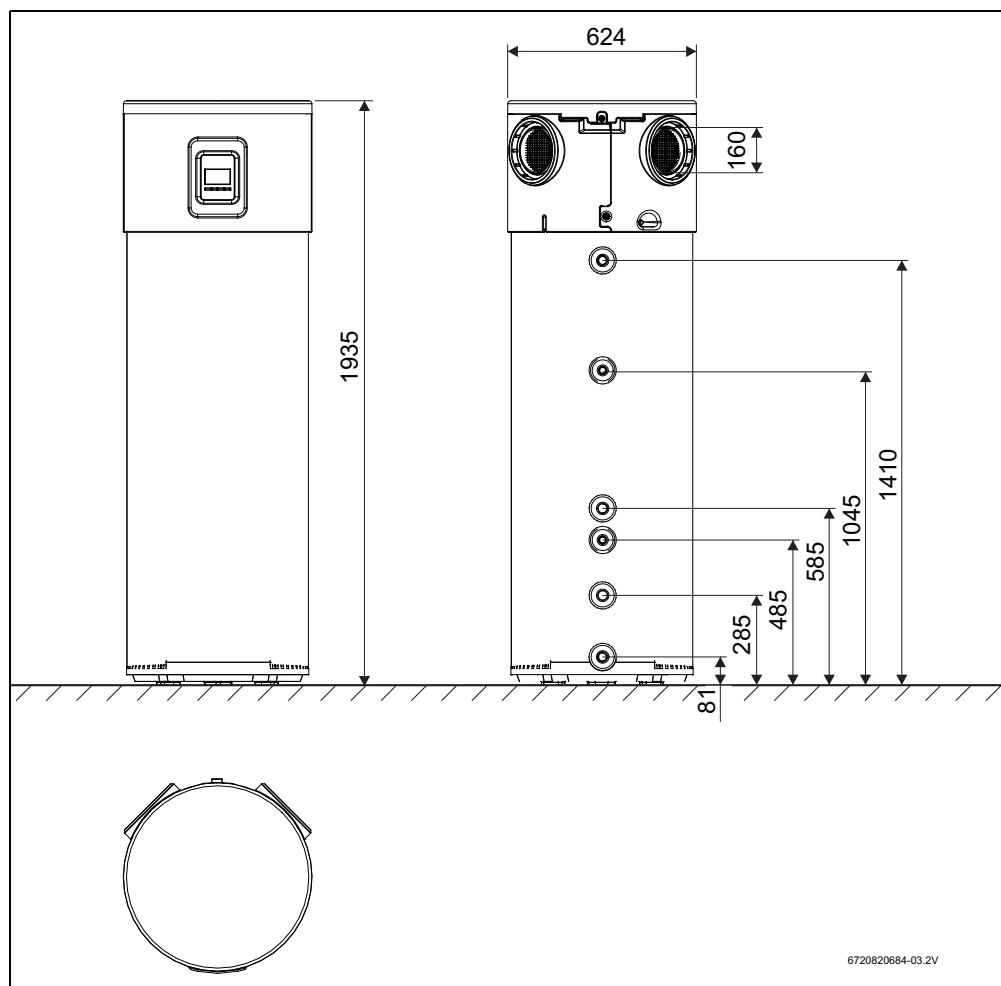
Dimensiones del aparato de 250 l (en mm)
